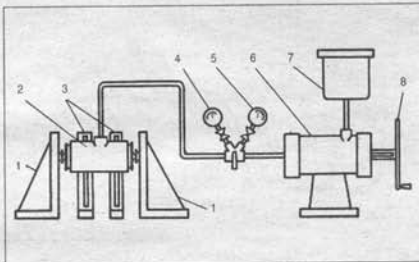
Схема проверки колесных цилиндров задних тормозов: 1 – упоры поршней; 2 – испытываемый цилиндр; 3 – кронштейн цилиндра; 4 – манометр низкого давления; 5 – манометр высокого давления; 6 – цилиндр для создания давления; 7 – емкость; 8 – маховик
